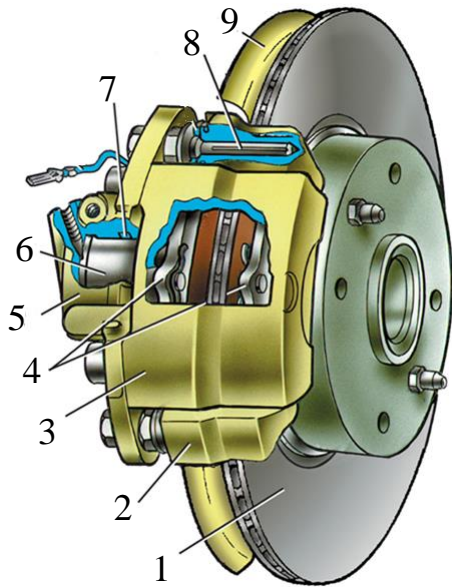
Дисковый тормозной механизм с плавающей скобой: 1 – тормозной диск; 2 – направляющая колодок; 3 – суппорт; 4 – тормозные колодки; 5 – цилиндр; 6 – поршень; 7 – уплотнительное кольцо; 8 – направляющий палец; 9 – защитный кожух
